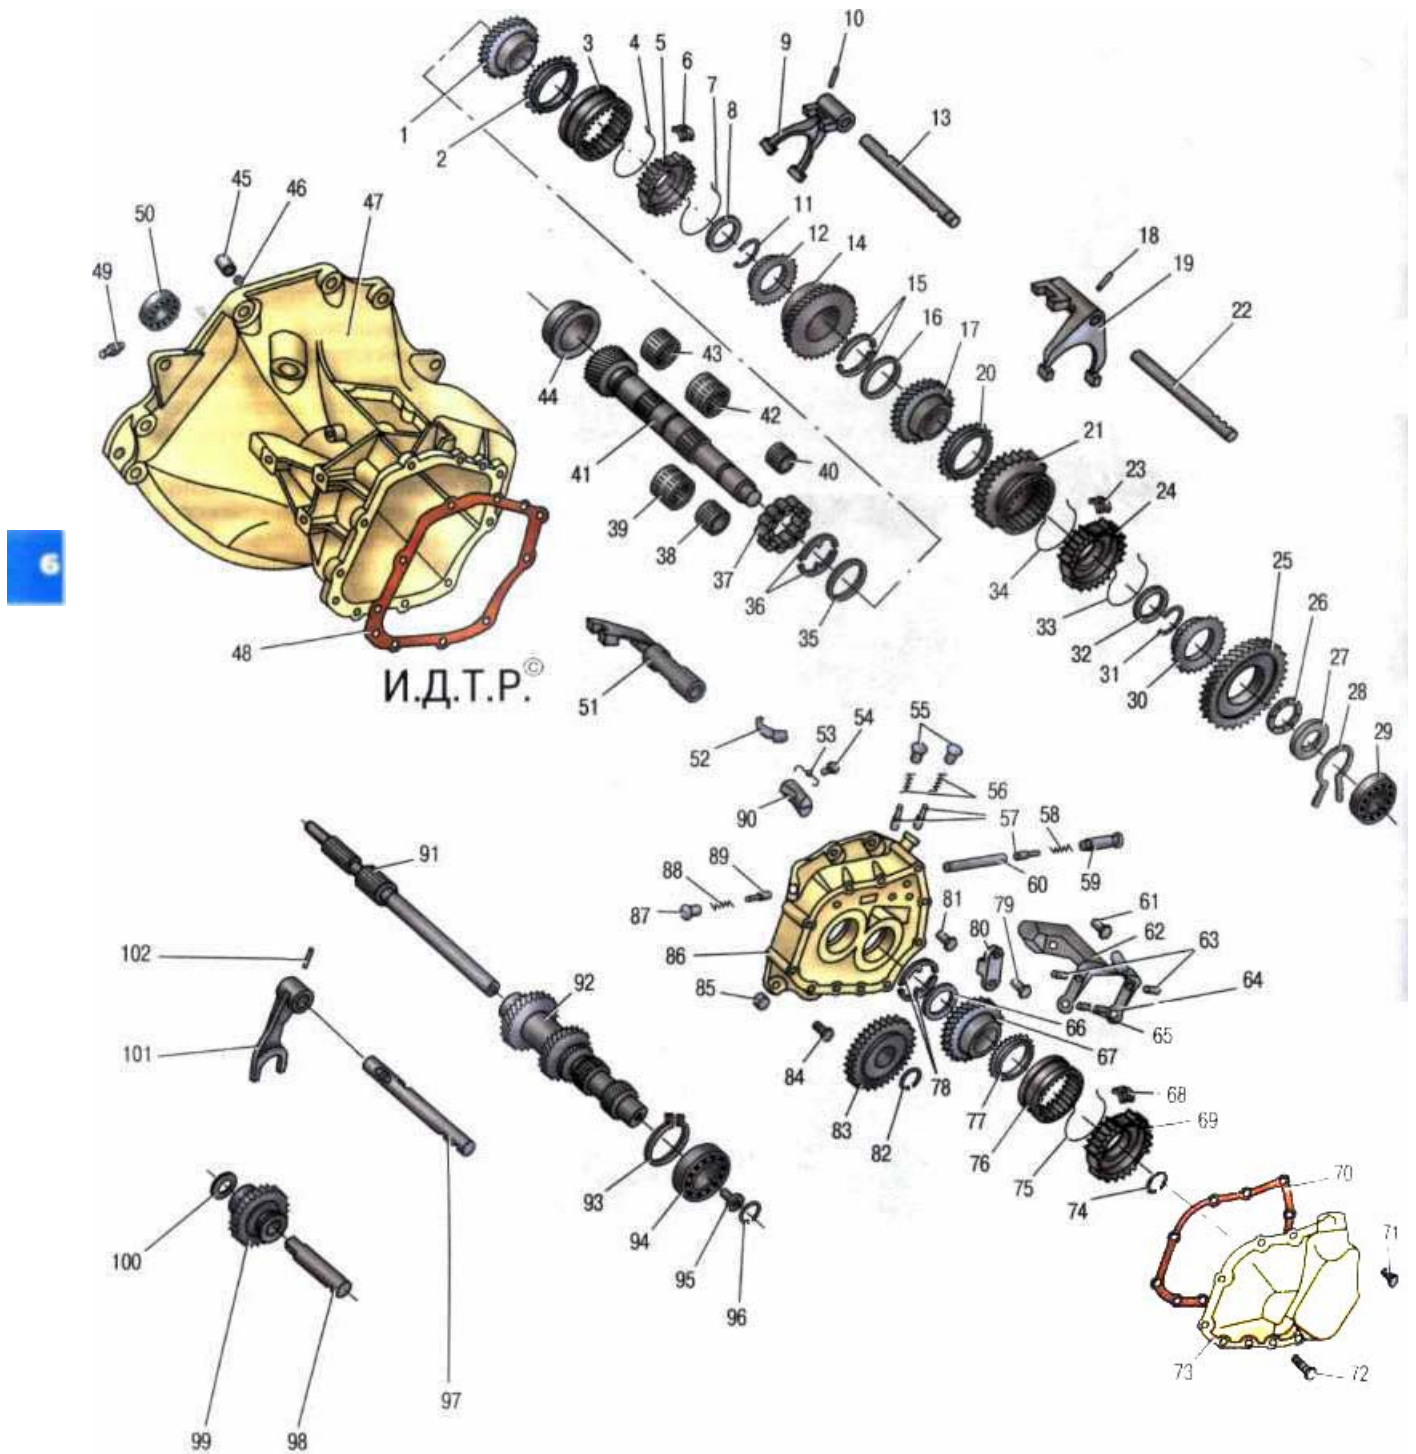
Коробка передач: 1 - шестерня IV передачи; 2, 12, 20, 30, 77 - блокирующие кольца синхронизаторов; 3 - муфта включения синхронизаторов III и IV передач; 4, 7, 33, 34, 75 - пружинные кольца синхронизатора; 5 - ступица синхронизатора III и IV передач; 6, 23, 68 - сухари синхронизатора; 8, 32 - упорные шайбы; 9 - вилка переключения III и IV передач; 10, 18, 102 - штифты; 11, 31, 74, 82, 93, 96 - стопорные кольца; 13 - шток вилки переключения III и IV передач; 14 - шестерня III передачи; 15, 36, 78 - упорные полукольца; 16, 35, 66 - запорные кольца; 17 - шестерня II передачи; 19 - вилка переключения I и II передач; 21 - муфта включения синхронизатора I и II передач; 22 - шток вилки переключения I и II передач; 24 - ступица синхронизаторов I и II передач; 25 - шестерня I передачи; 26 - упорный игольчатый подшипник шестерни I передачи; 27 - опорная шайба; 28 - пружинное кольцо; 29 - подшипник вторичного вала; 37 - роликовый подшипник вторичного вала; 38 - игольчатый подшипник шестерни I передачи; 39 - игольчатый подшипник шестерни II передачи; 40 - игольчатый подшипник шестерни V передачи; 41 - вторичный вал; 42 - игольчатый подшипник шестерни III передачи; 43 - игольчатый подшипник шестерни IV передачи; 44 - наружное кольцо роликового подшипника вторичного вала; 45 - пробка; 46 - магнит; 47 - картер коробки передач; 48 - прокладка картера коробки передач; 49 - выключатель фонарей света заднего хода; 50 - роликовый подшипник первичного вала; 51 - поводок с подшипником V передачи; 52 - собачка; 53 - пружина собачки; 54, 61, 71, 72, 79, 81, 84 - болты; 55, 59, 87 - пробки фиксаторов; 56, 58, 88 - пружины; 57, 89 - фиксаторы; 60 - штифт механизма блокировки; 62 - кронштейн вилки включения V передачи; 63 - ось вилки включения V передачи; 64 - вилка включения V передачи; 65 - сухари вилки; 67 - ведомая шестерня V передачи; 69 - ступица синхронизатора V передачи; 70 - прокладка крышки; 73 - крышка коробки передач; 76 - муфта включения синхронизатора V передачи; 80 - кронштейн собачки; 83 - ведущая шестерня V передачи; 85 - магнит; 86 - промежуточный картер; 90 - кронштейн собачки; 91 - первичный вал; 92 - блок шестерен; 94 - шариковый подшипник блока шестерен; 95 - винт; 97 шток вилки включения промежуточной шестерни заднего хода; 98 - ось промежуточной шестерни заднего хода; 99 - промежуточная шестерня заднего хода; 100 - шайба; 101 - вилка включения промежуточной шестерни заднего хода
